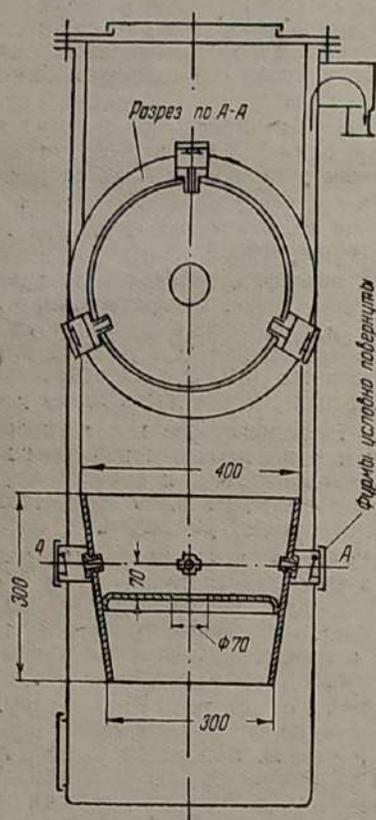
Схема древесного газогенератора Г-42 с топливником конструкции инж. Высотского
